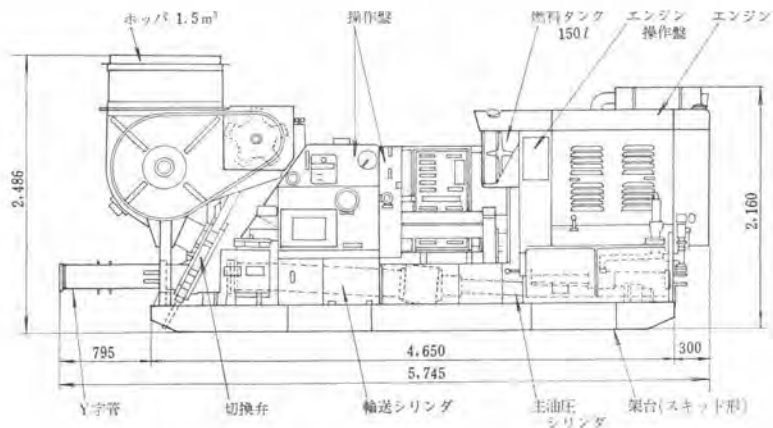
コンクリートポンプ（最大骨材径 80 mm 用）略図
